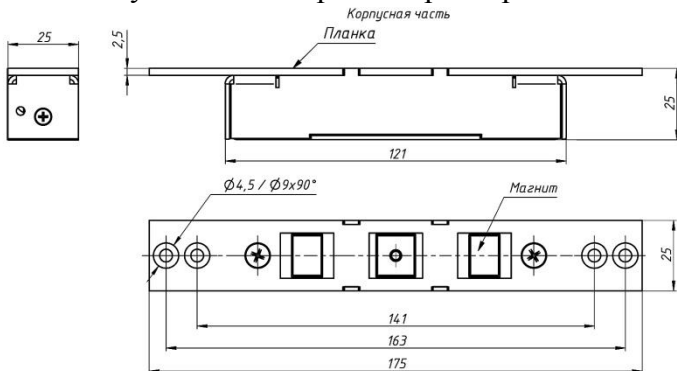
Габаритные размеры ЭМЗ-1500
